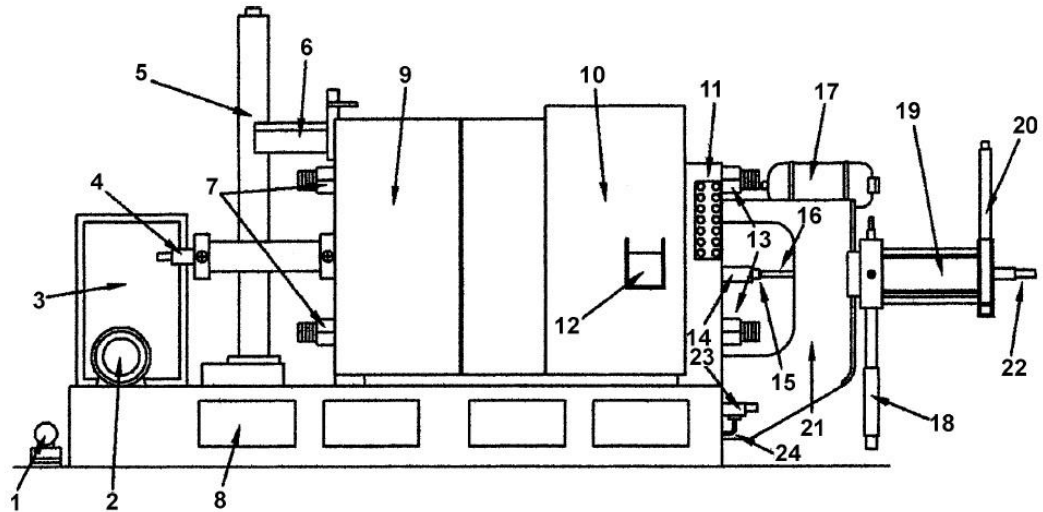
4 Soğuk kamaralı basınçlı döküm makinesinde işlem çevrimi [8]
